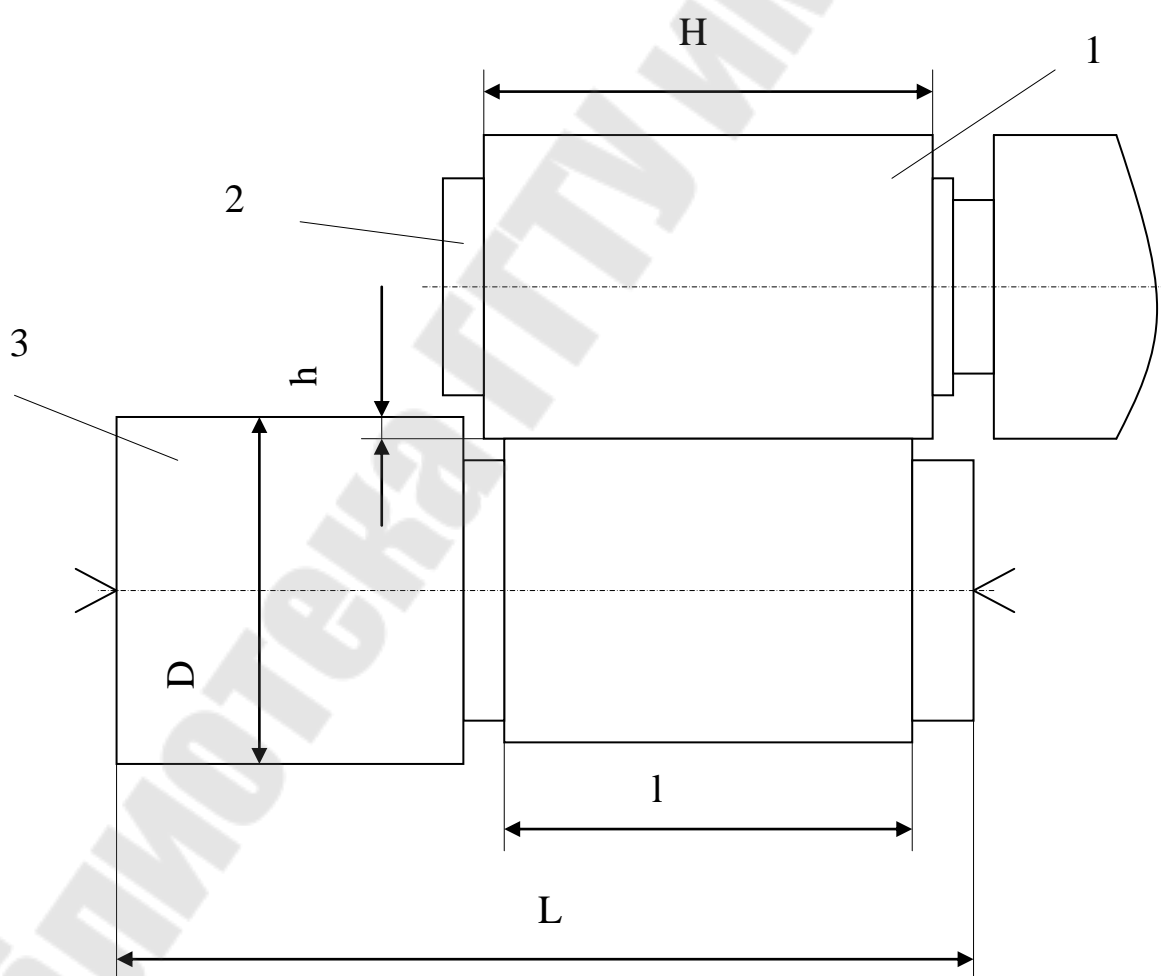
Схема установки заготовки детали на шлифовальном станке
